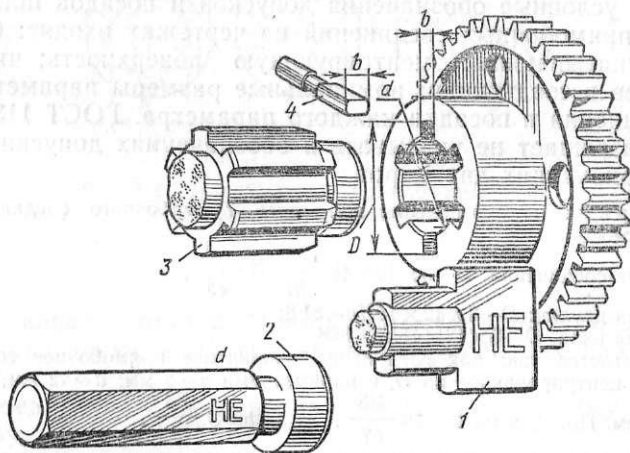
Калибры для контроля шлицевого прямоугольного отверстия:
